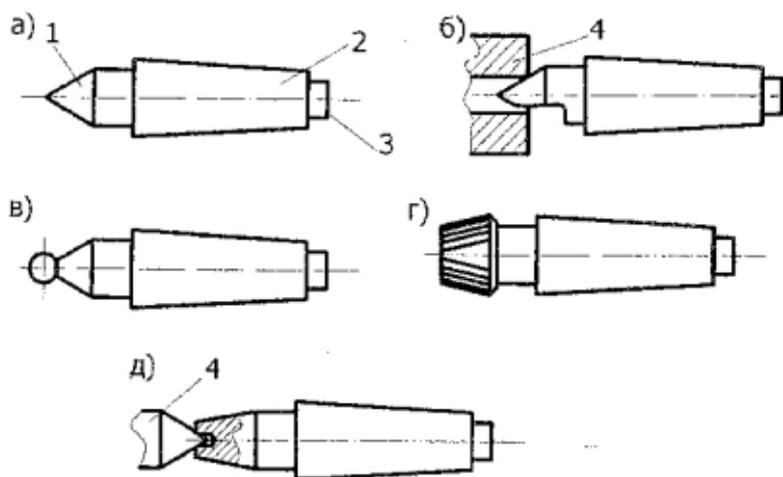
Основные конструкции центров: а – упорный (нормальный) центр; б – срезанный центр; в- шариковый центр; г – рифленный центр; д – обратный центр; 1 – рабочая часть; 2 0 хвостовая часть; 3 – опорная часть; 4 – устанавливаемая заготовка.
